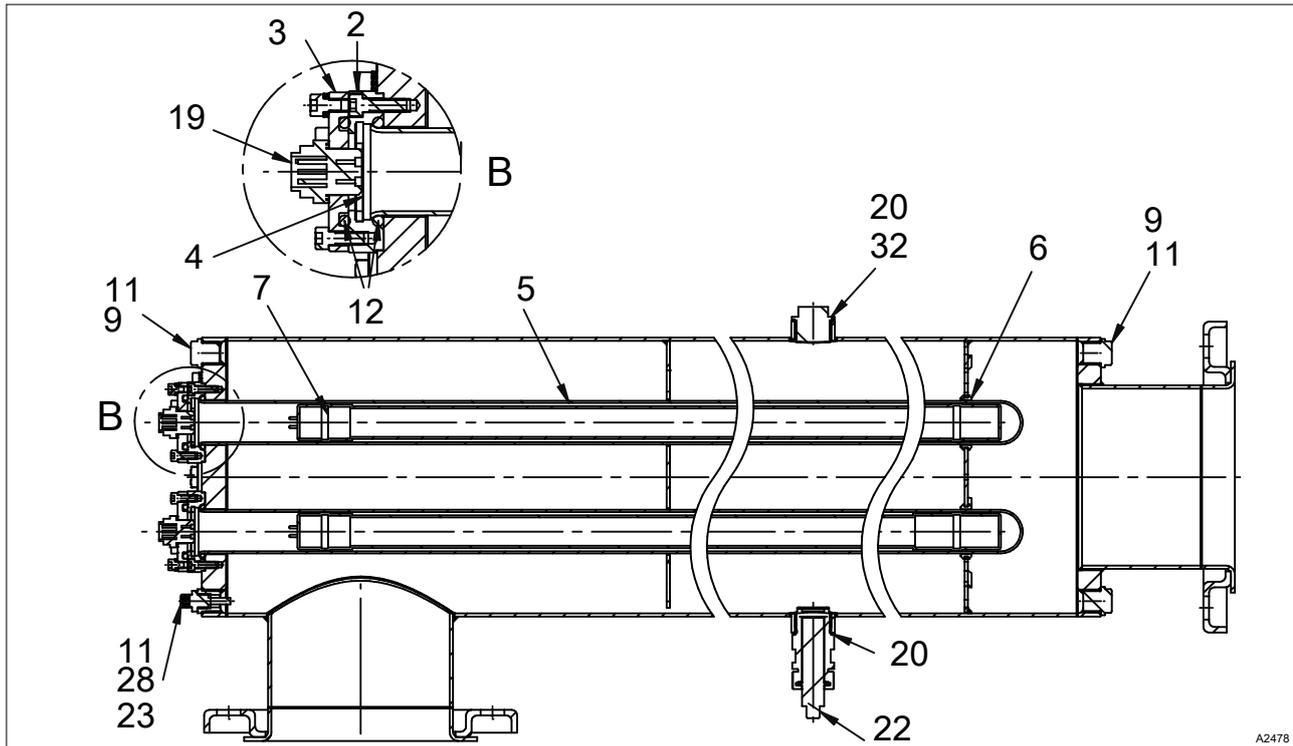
Pièces de rechange, 6x350 W, installation à six lampes sans dispositif d'essuyage
